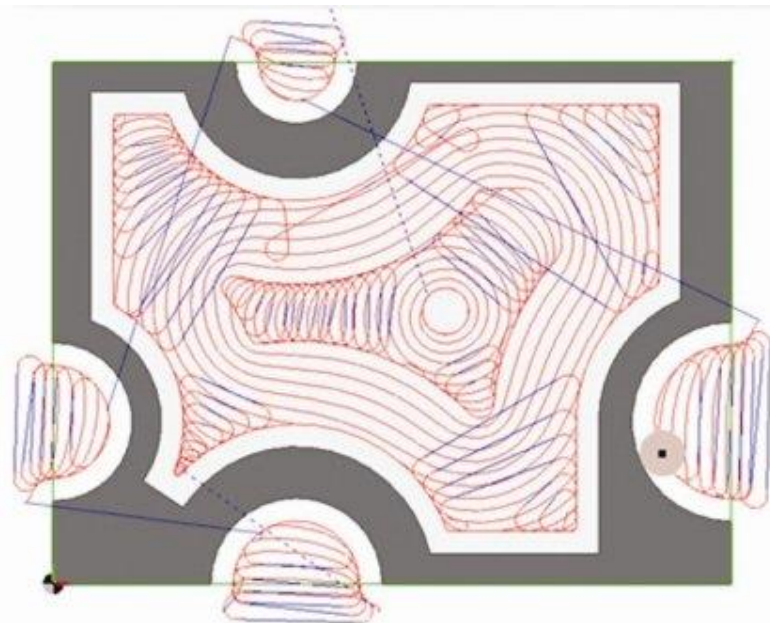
Vizualizace dráhy nástroje vygenerované metodou TrueMill [36]
